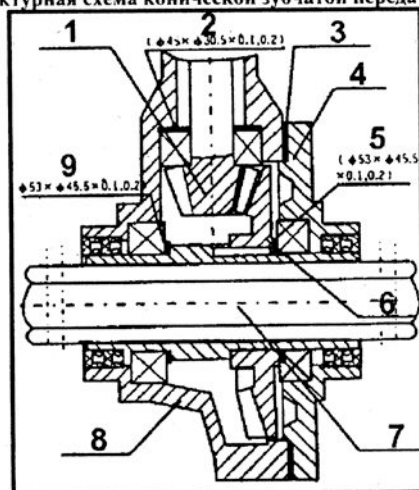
Структурная схема конической зубчатой передачи в корпусе трансмиссии:
